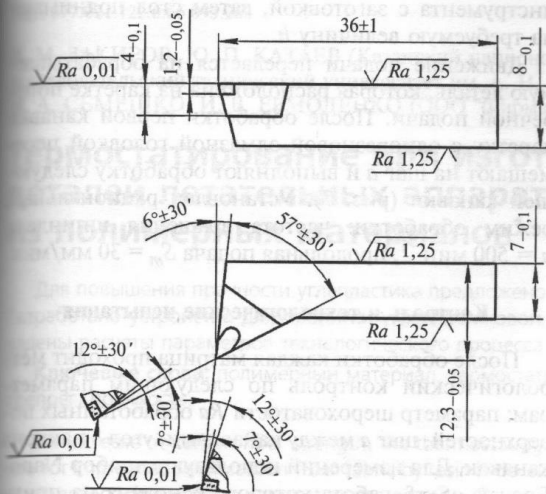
Алмазный резец для обработки матриц для Френелевских призм
